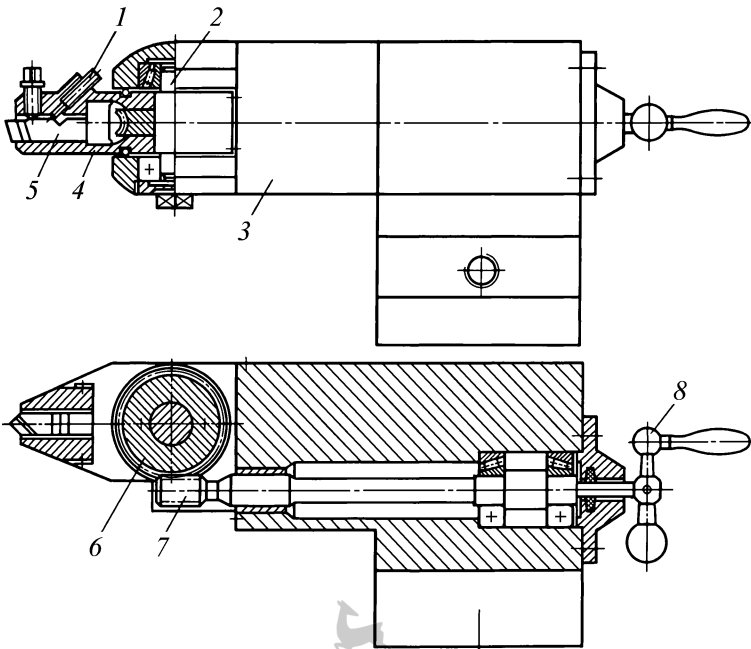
Расточная оправка для обработки внутренних сферических и торцовых поверхностей:
